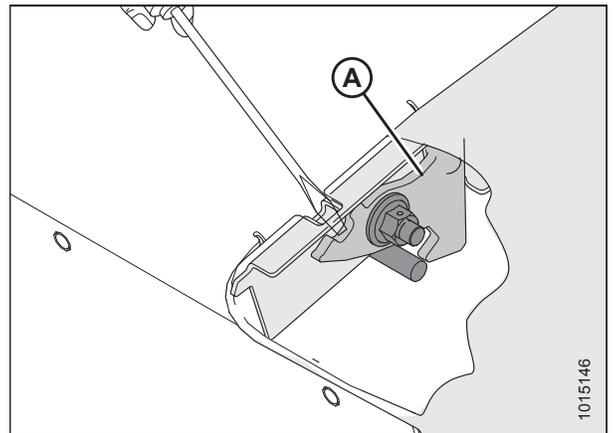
Verrou de porte de barre de coupe – vue en coupe
